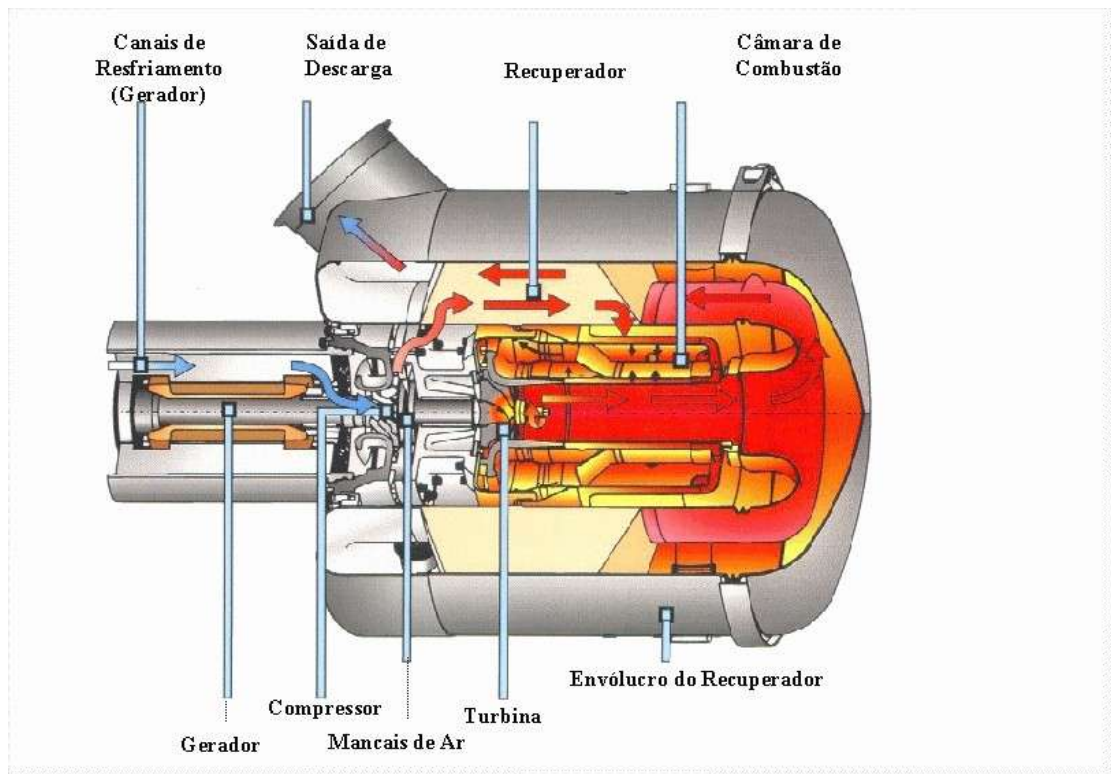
Detalhe em Corte da Câmara de Combustão da Turbina Capstone
